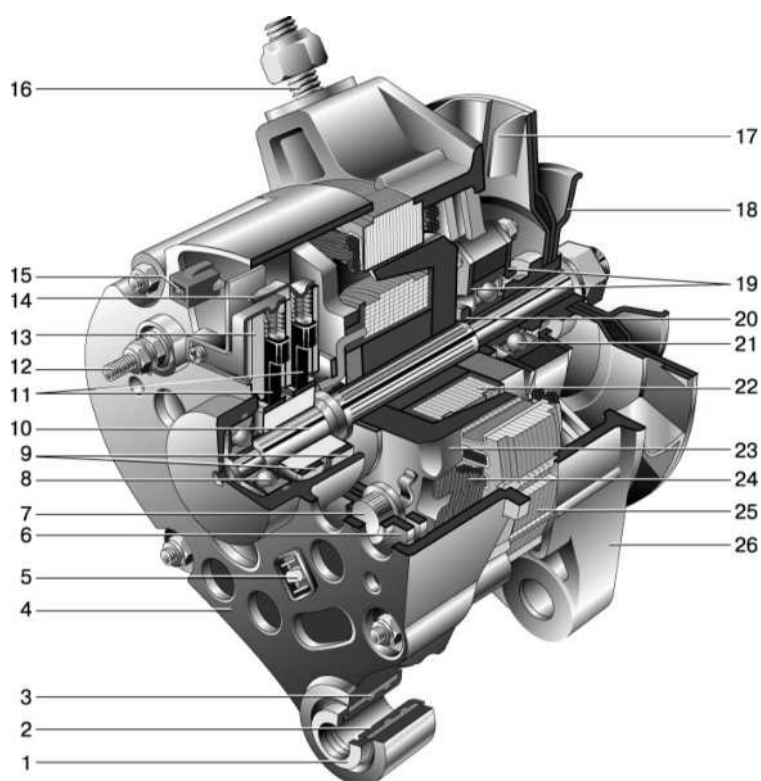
Устройство генератора Г-221: 1 – поджимная втулка; 2 – втулка; 3 – буферная втулка; 4 – задняя крышка; 5 – винт крепления выпрямительного блока; 6 – выпрямительный блок; 7 – вентиль (диод); 8 – задний подшипник; 9 – контактные кольца; 10 – вал ротора; 11 – щетки; 12 – вывод «30»; 13 – щеткодержатель; 14 – вывод «67»; 15 – штекер нулевого провода; 16 – шпилька крепления генератора; 17 – крыльчатка вентилятора; 18 – шкив; 19 – пластины; 20 – кольцо; 21 – передний подшипник; 22 – обмотка ротора; 23 – ротор; 24 – обмотка статора; 25 – статор; 26 – передняя крышка.
